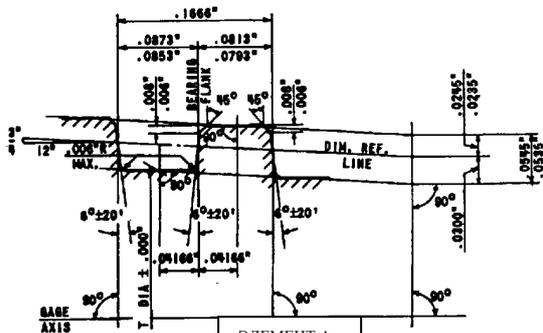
Конструкция калибров размером от 5 до  $7\frac{5}{8}$  дюйма
